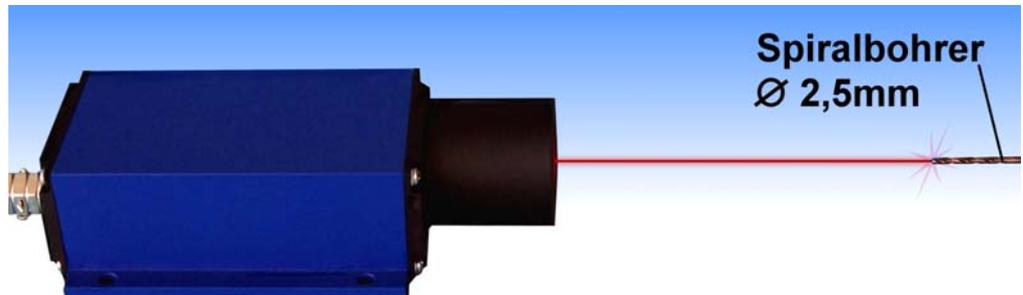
Laserdistanzsensor LDS-2 zur Werkzeugbruchkontrolle mit Auswertung der Laufzeit des vom Werkzeug reflektierten Lichtes
